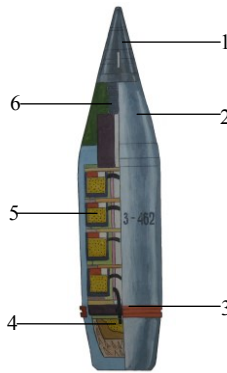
Запалювальний снаряд: 1 – дистанційний підричник; 2 – корпус із пригвинтною головкою; 3 – ведучий пояс; 4 – вибивний заряд; 5 – запалювальні елементи; 6 – діафрагма зі сповільнювачем
